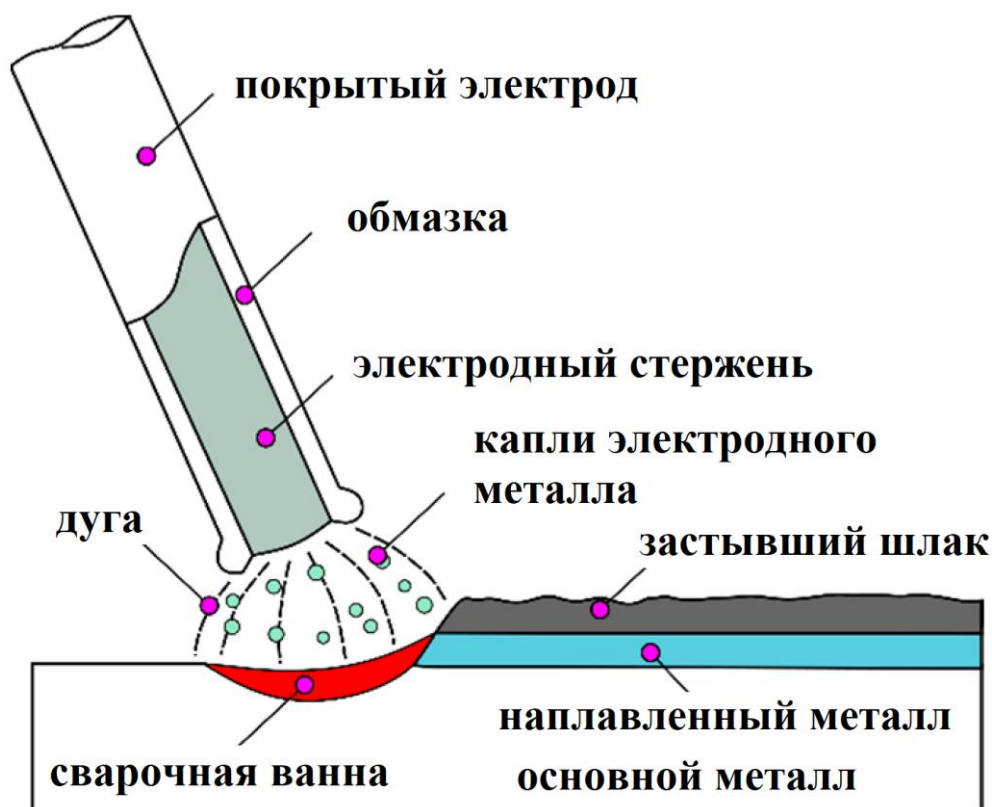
Схема выполнения ручной дуговой сварки
